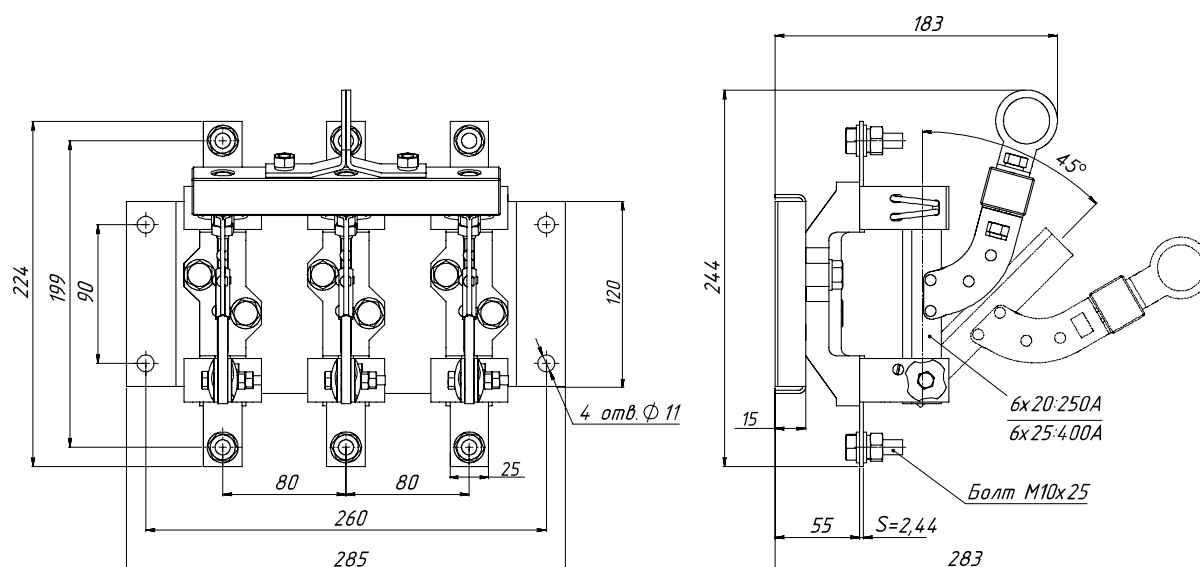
Разъединитель РЕ19-35(37)-31190-00 УХЛЗ с центральным рычагом для управления штангой
